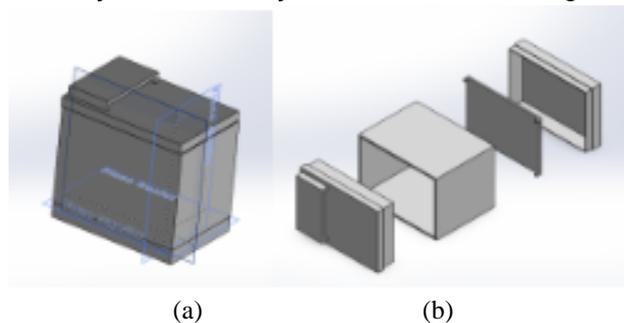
Sistema de captura de imagens. (a) sistema montado. (b) visão explodida.
